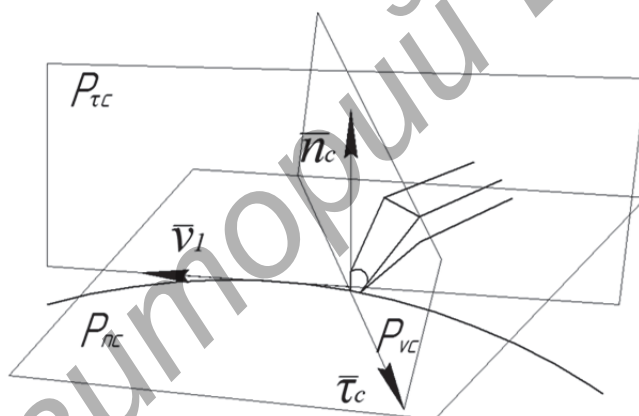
Положение инструмента на сферической поверхности в статической системе координат
